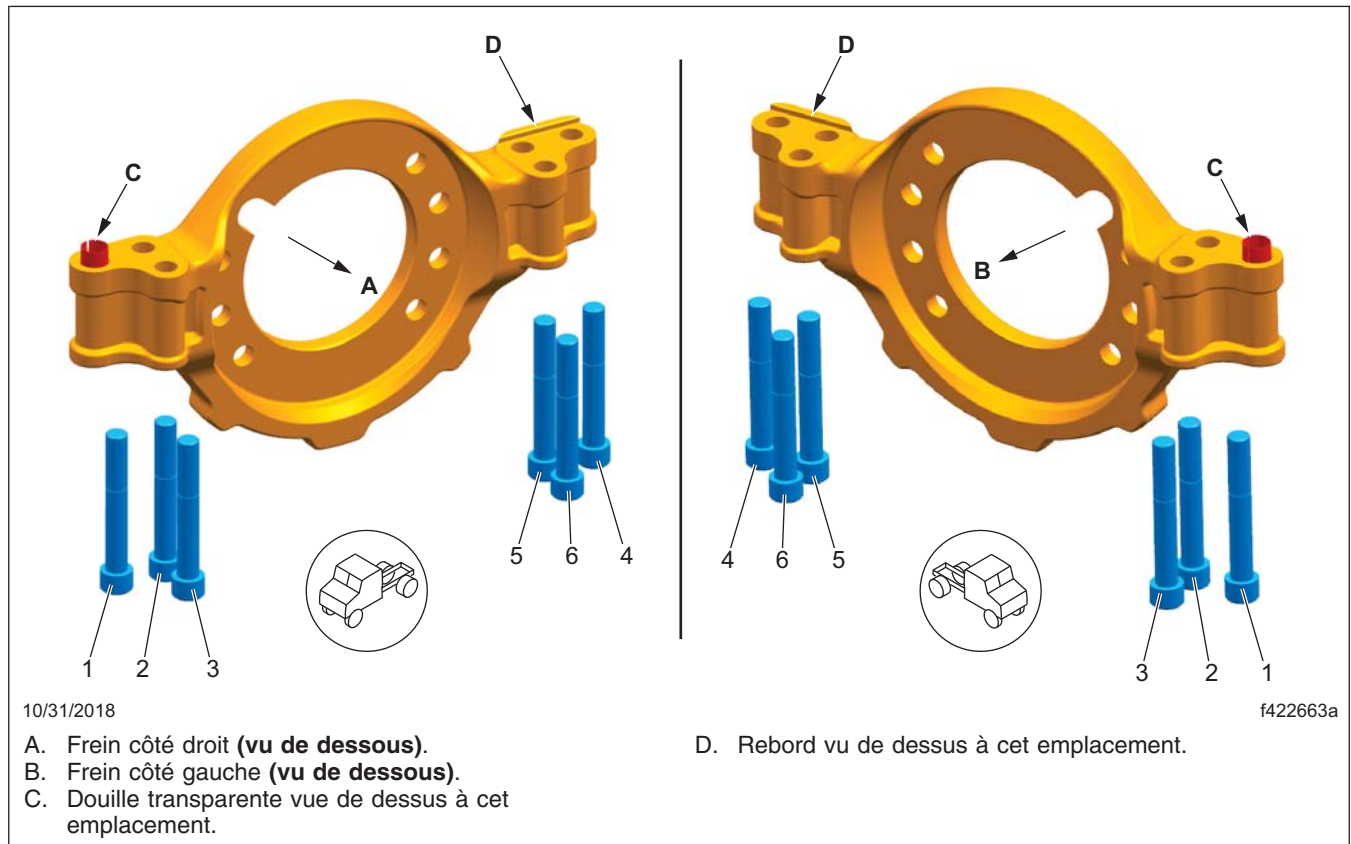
, Ordre de serrage (vue de dessous), étrier Bendix à montage radial
